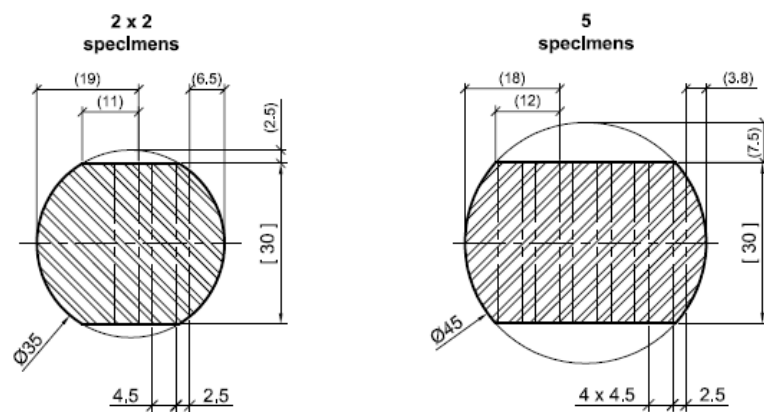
Ilustração do aproveitamento de cada secção do tarugo para obter as amostras para a soldadura (dimensões em mm).
